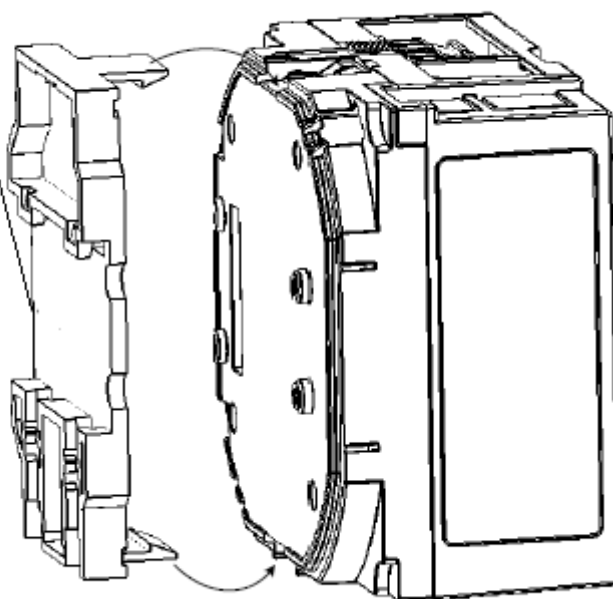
Схема крепления адаптера для DIN-рейки
